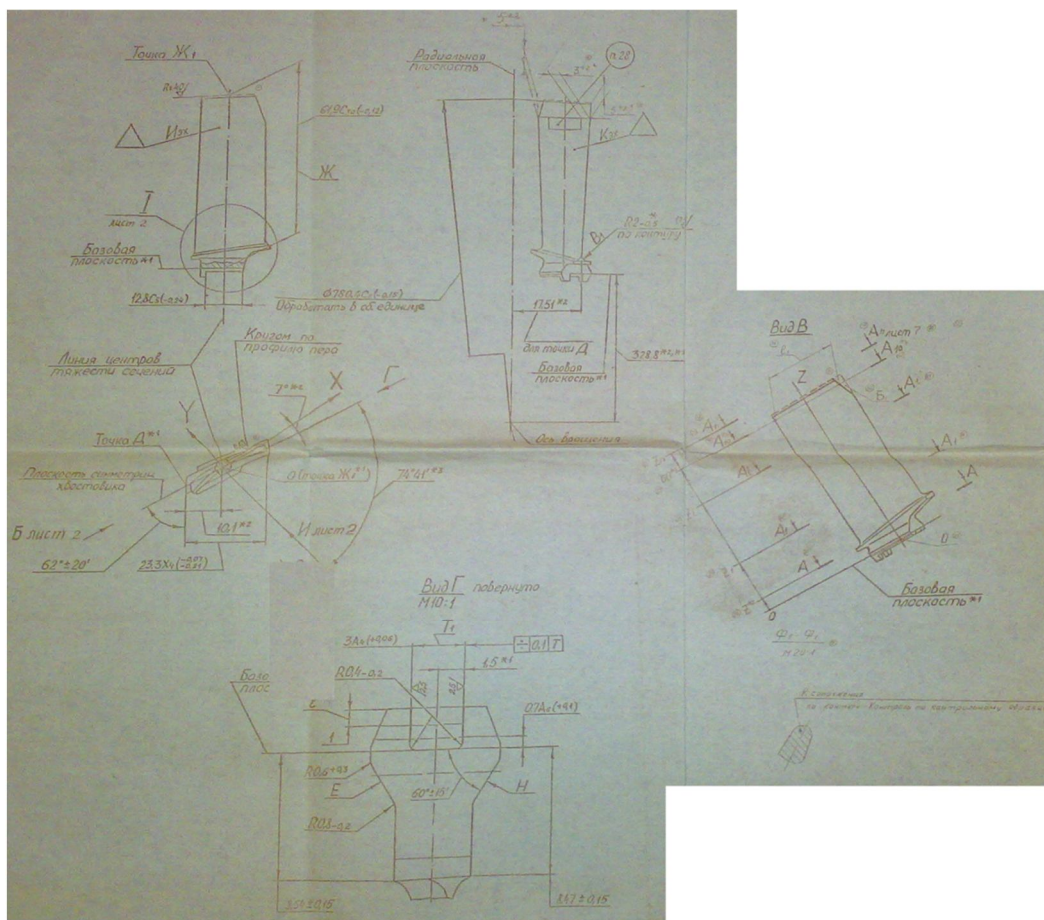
Фото кресления лопатки компрессора ТРД (Лист 2)
